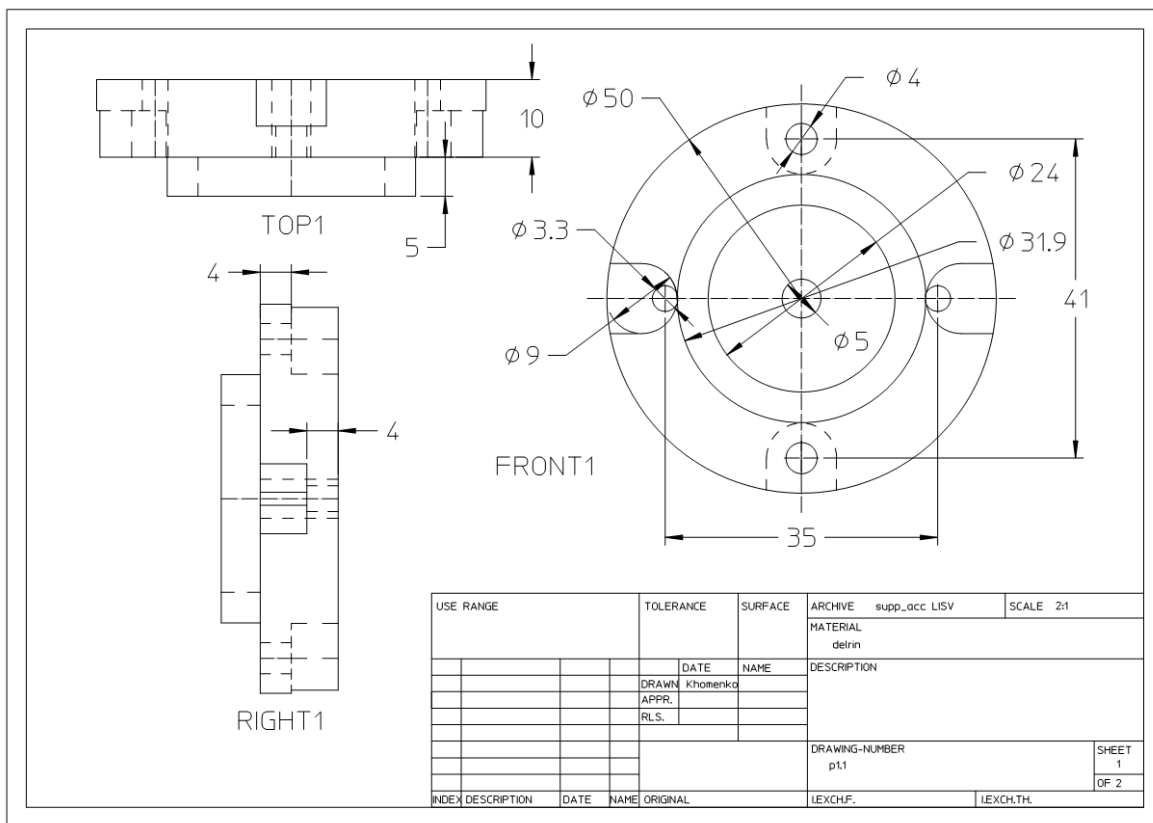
Dessin technique de la pièce réalisée pour supporter l'accéléromètre sur la cheville
